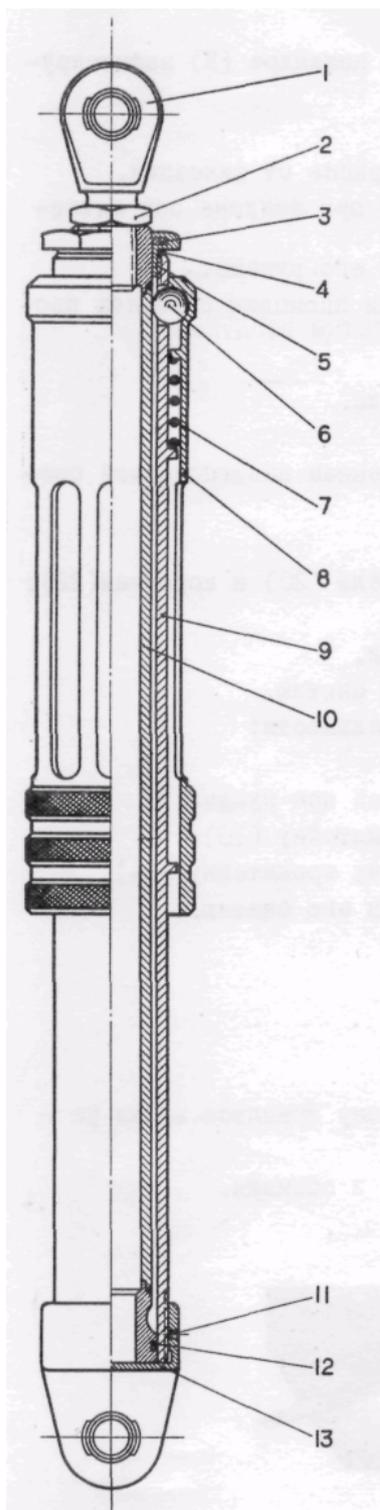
УПОРНЫЙ ЦИЛИНДР
